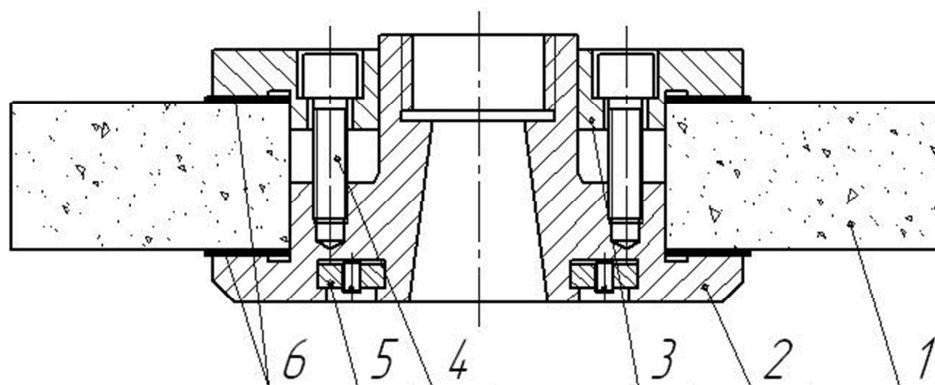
Крепление шлифовальных кругов на планшайбе:
